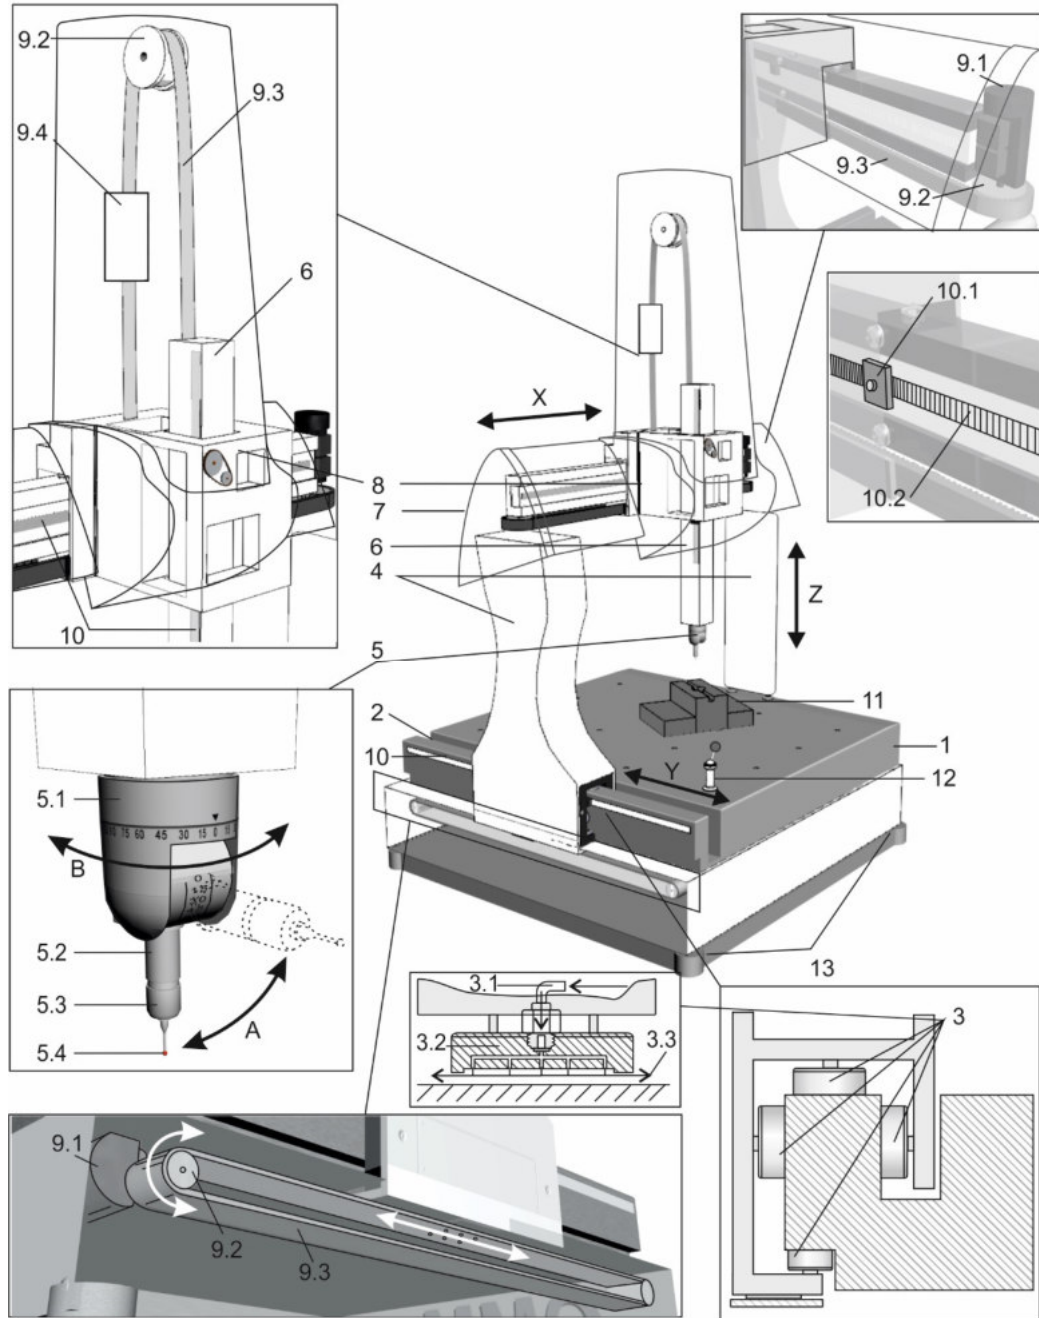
Особенности конструкции КИМ, где: 1 – гранитное основание; 2 – направляющие поверхности на основании для перемещений портала; 3 – аэростатические подшипники портала: подвод сжатого воздуха (3.1), корпус с пневмоканалами (3.2), «воздушная подушка» (3.3); 4 - стойки портала; 5 – измерительная головка: поворотный узел (5.1), удлинитель датчика ИГ (5.2), датчик (5.3), измерительный наконечник (5.4); 6 - пиноль; 7 - балка портала; 8 - каретка; 9 – привода УКП X, Y, Z: электродвигатель (9.1), приводной ролик (9.2), армированная лента (9.3), противовес пиноты (9.4); 10 - измерительные преобразователи перемещений (линейные энкодеры): оптическая считывающая головка (10.1), линейная шкала (10.2); 11 - измеряемая деталь; 12 - калибровочная сфера; 13 -виброизолирующие опоры
